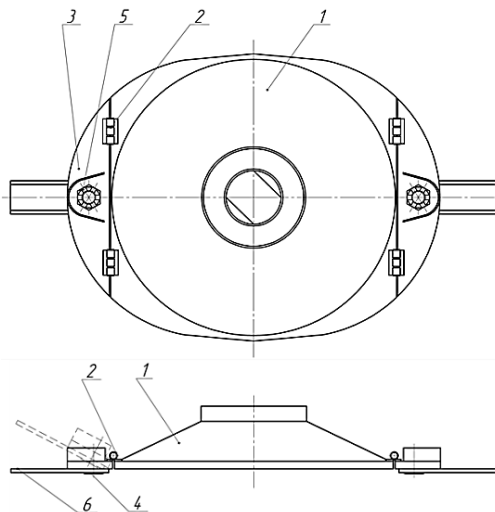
Модернизированный ротор косилки: 1 – центральная часть ротора; 2 – петли; 3 – периферийная часть ротора; 4 – болт крепления; 5 – гайка; 6 – нож
